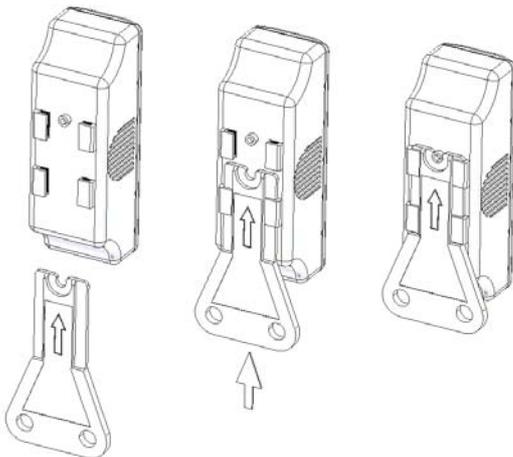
Aufstecken des Sensors auf den Befestigungshalter
